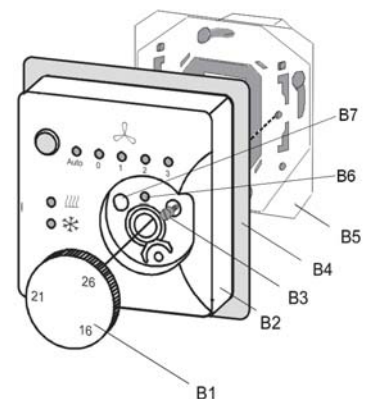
Montage des Fan-Coil Unit Bediengerätes
